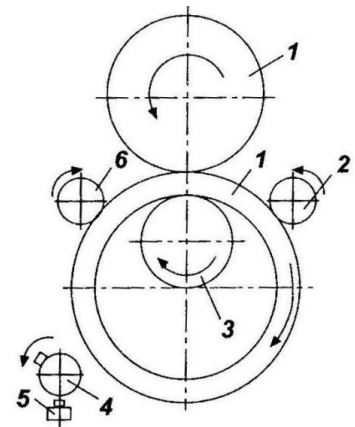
Схема розкатування кільцевих заготовок: 1 – розкатувальний валок; 2, 6 – напрямні ролики; 3 – притискний валок; 4 – контрольний ролик; 5 – кінцевий вимикач; 7 – заготовка
